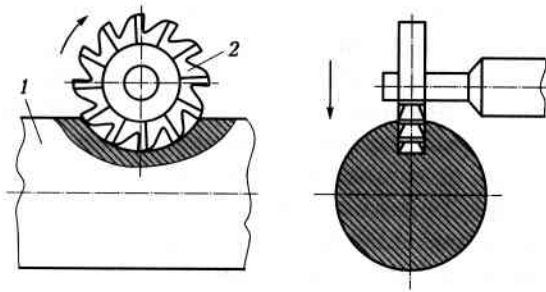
Схема фрезерования шпоночной канавки для сегментной шпонки:
